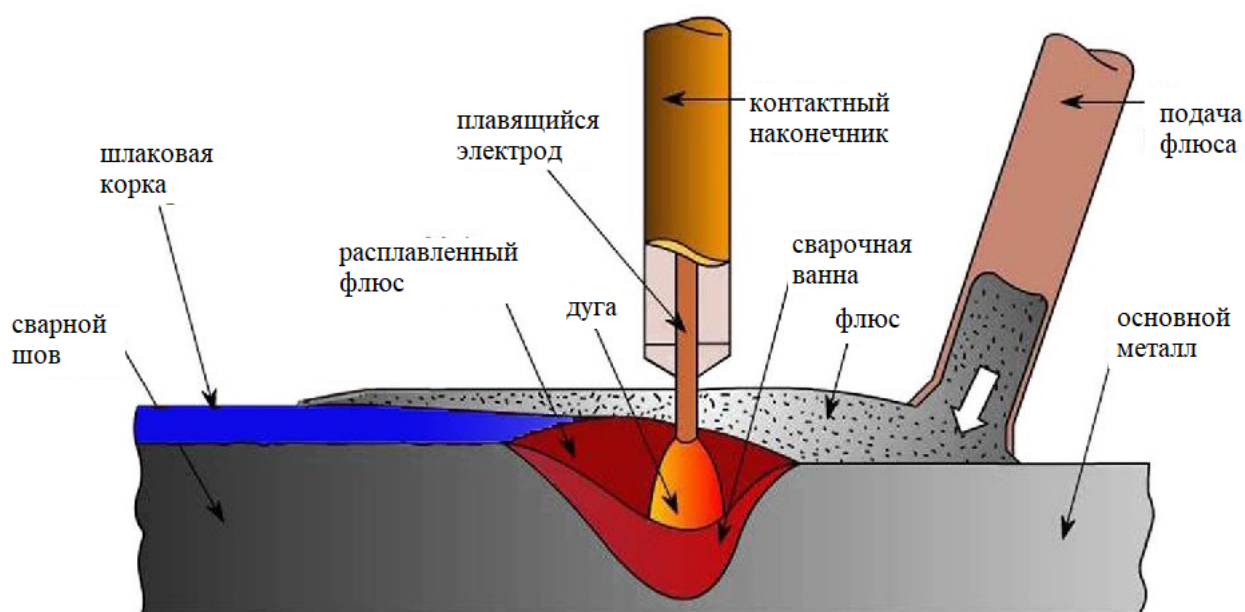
Схема выполнения автоматической сварки под флюсом
